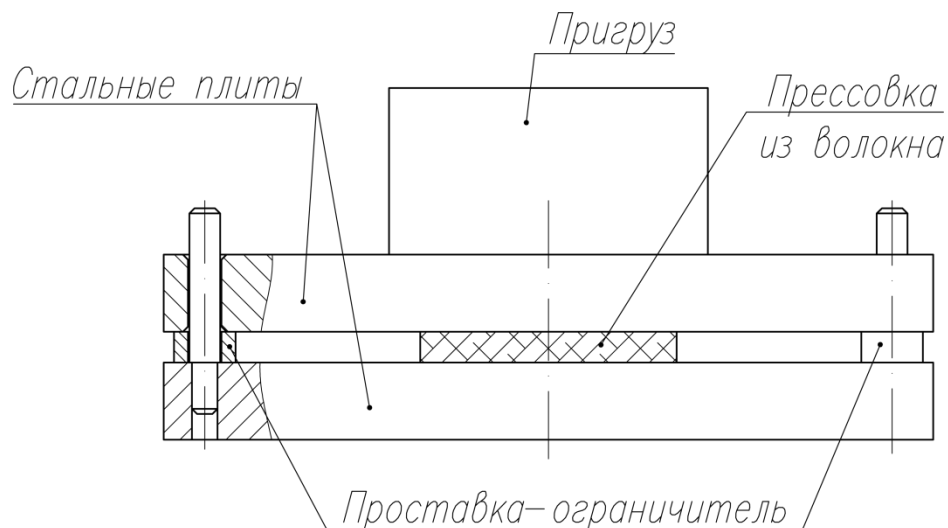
Схема приспособления для диффузионной сварки образцов
